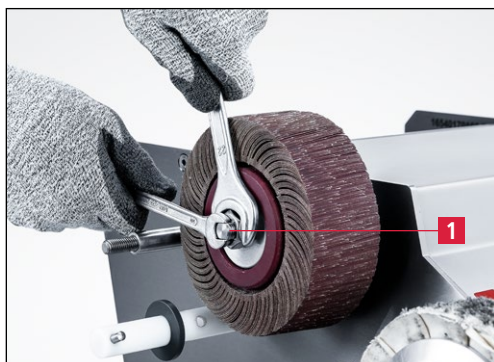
Освобождение пластинчатого шлифовального круга
